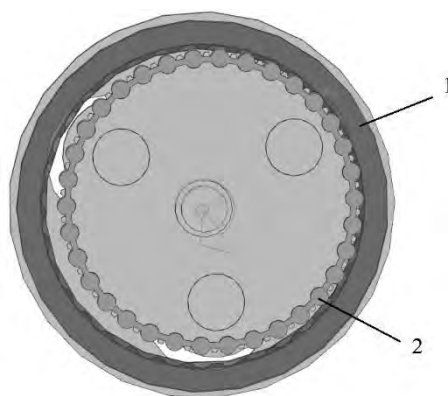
3D-модель планетарной цепной передачи типа К-Н-V
